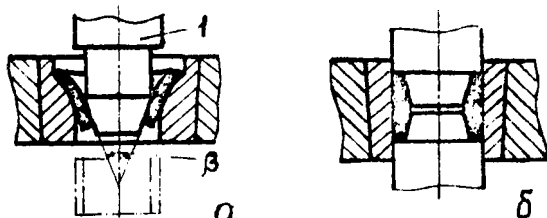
Схема технологического процесса изготовления втулок из шайбы способом вытяжки с разбортовкой: а - вытяжка с разбортовкой; б - формовка конических поверхностей.
